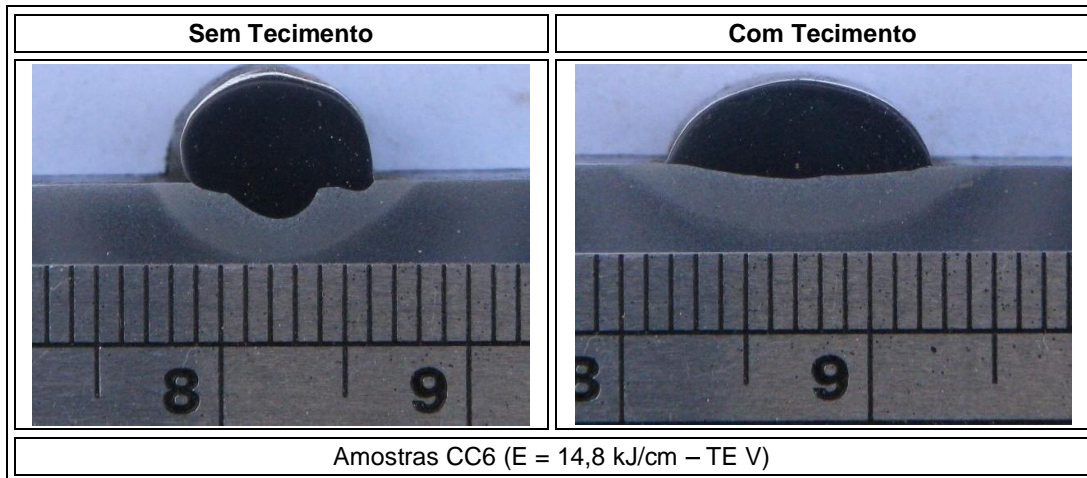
Seção transversal das amostras soldadas na condição CC6 com DPEP de 6 mm.
